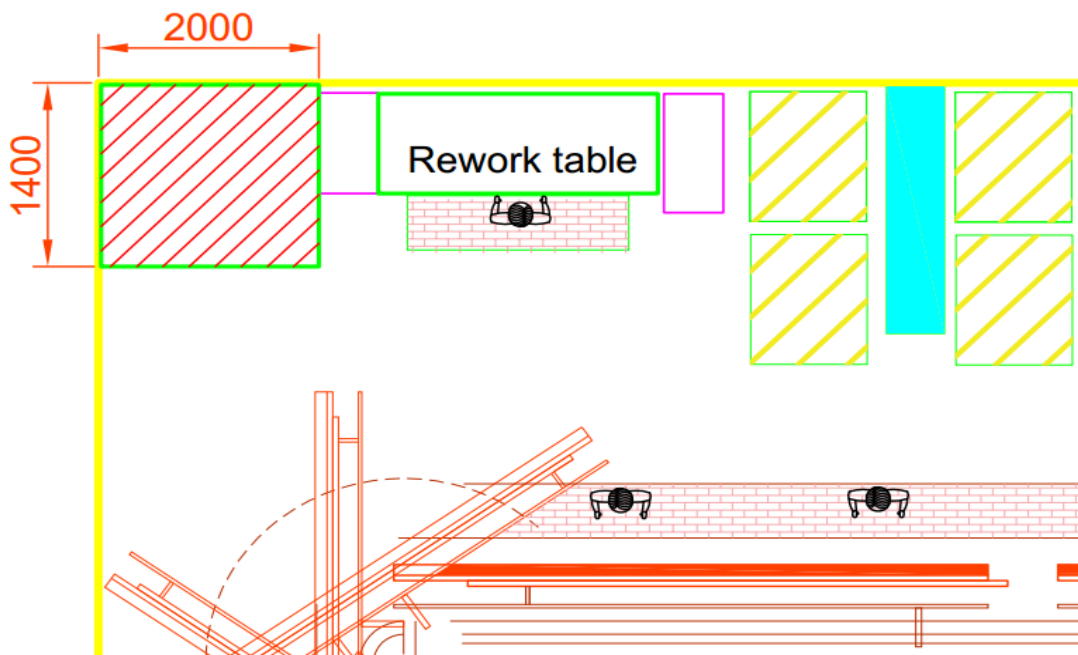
Gain de l'espace au niveau de la zone Floor line 2
